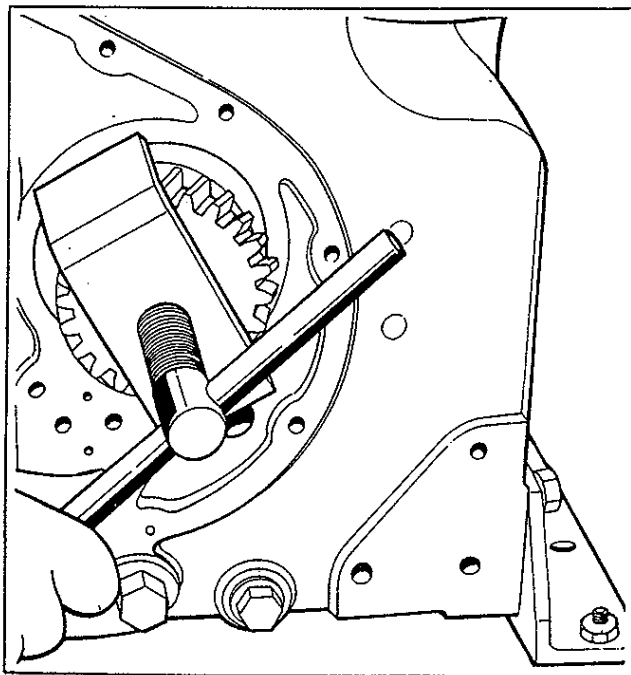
Desmontagem da engrenagem da árvore de manivela
